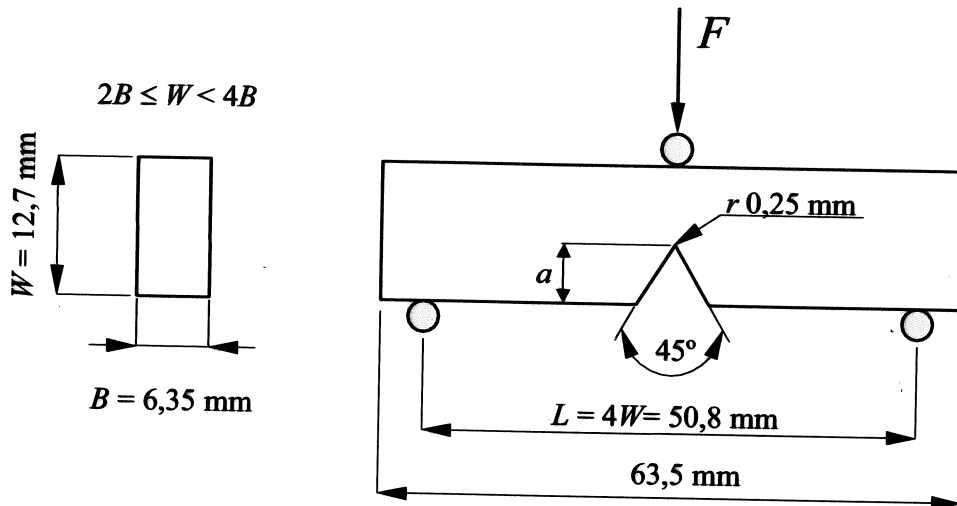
Probeta SENB (Single Edge Notched Bend) para ensayos de fractura.
